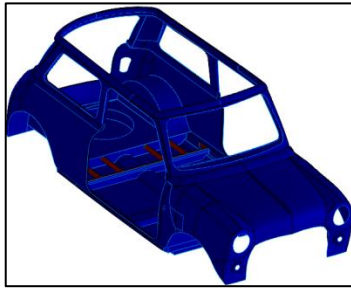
Modelado 3D de la carrocería de la MINIVAN.
